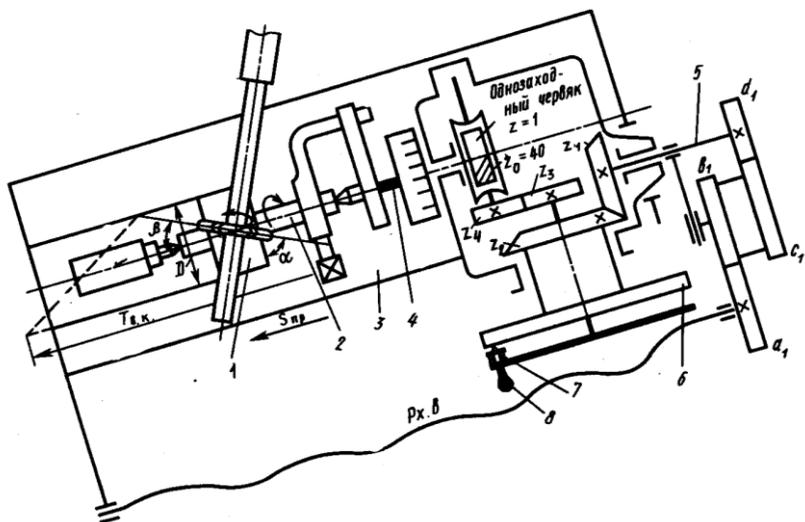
Схема наладки универсально-фрезерного станка и делительной головки на фрезерование винтовых канавок
